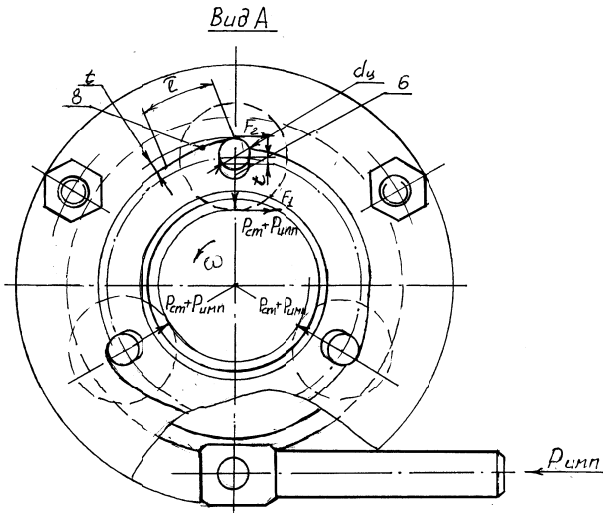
Вид А охватывающего инструмента для статико-импульсного упрочнения резьбы
